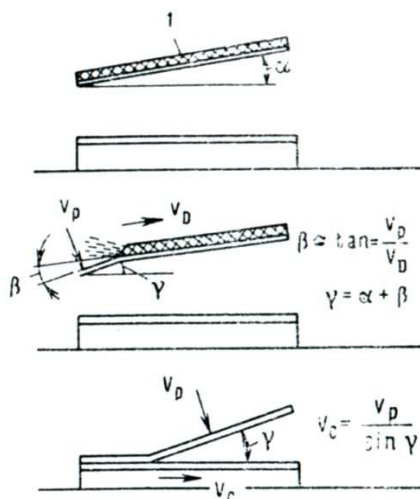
Схема установки для сварки взрывом при угловом расположении заряда и плиты: 1 - взрывчатое вещество а - исходный угол между верхней и нижней плитой
